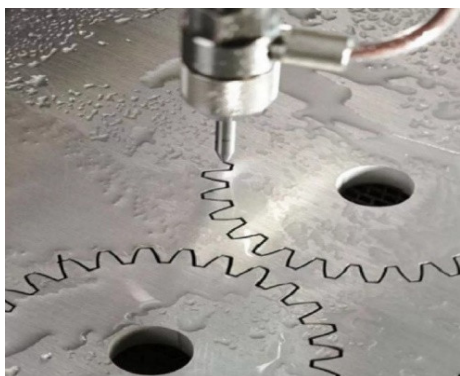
Изделия. Метод изготовления: гидроабразивная резка
